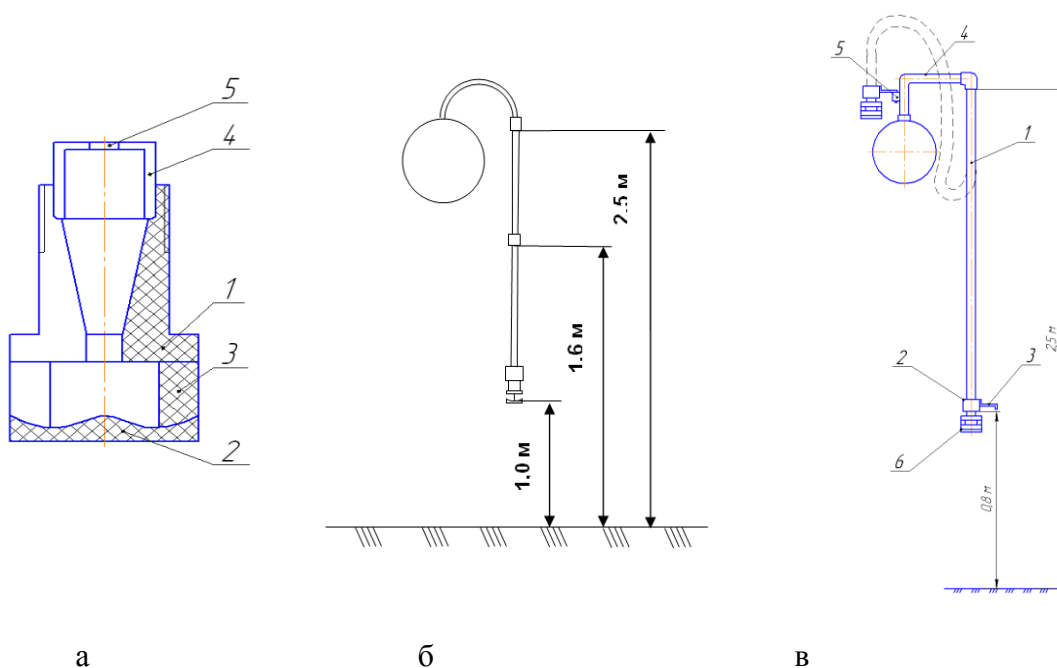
Дождевальная насадка с дефлектором «обратный конус» (а) и устройства приповерхностного полива типа «сборная штанга» (б) и «сборный рукав» (в)
